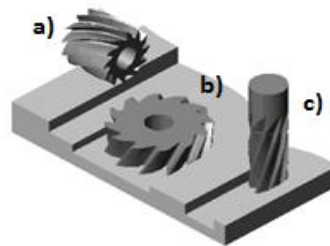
Fresagem: a) cilíndrica tangencial; b) cilíndrica frontal; c) topo; [ASM, 1987]
